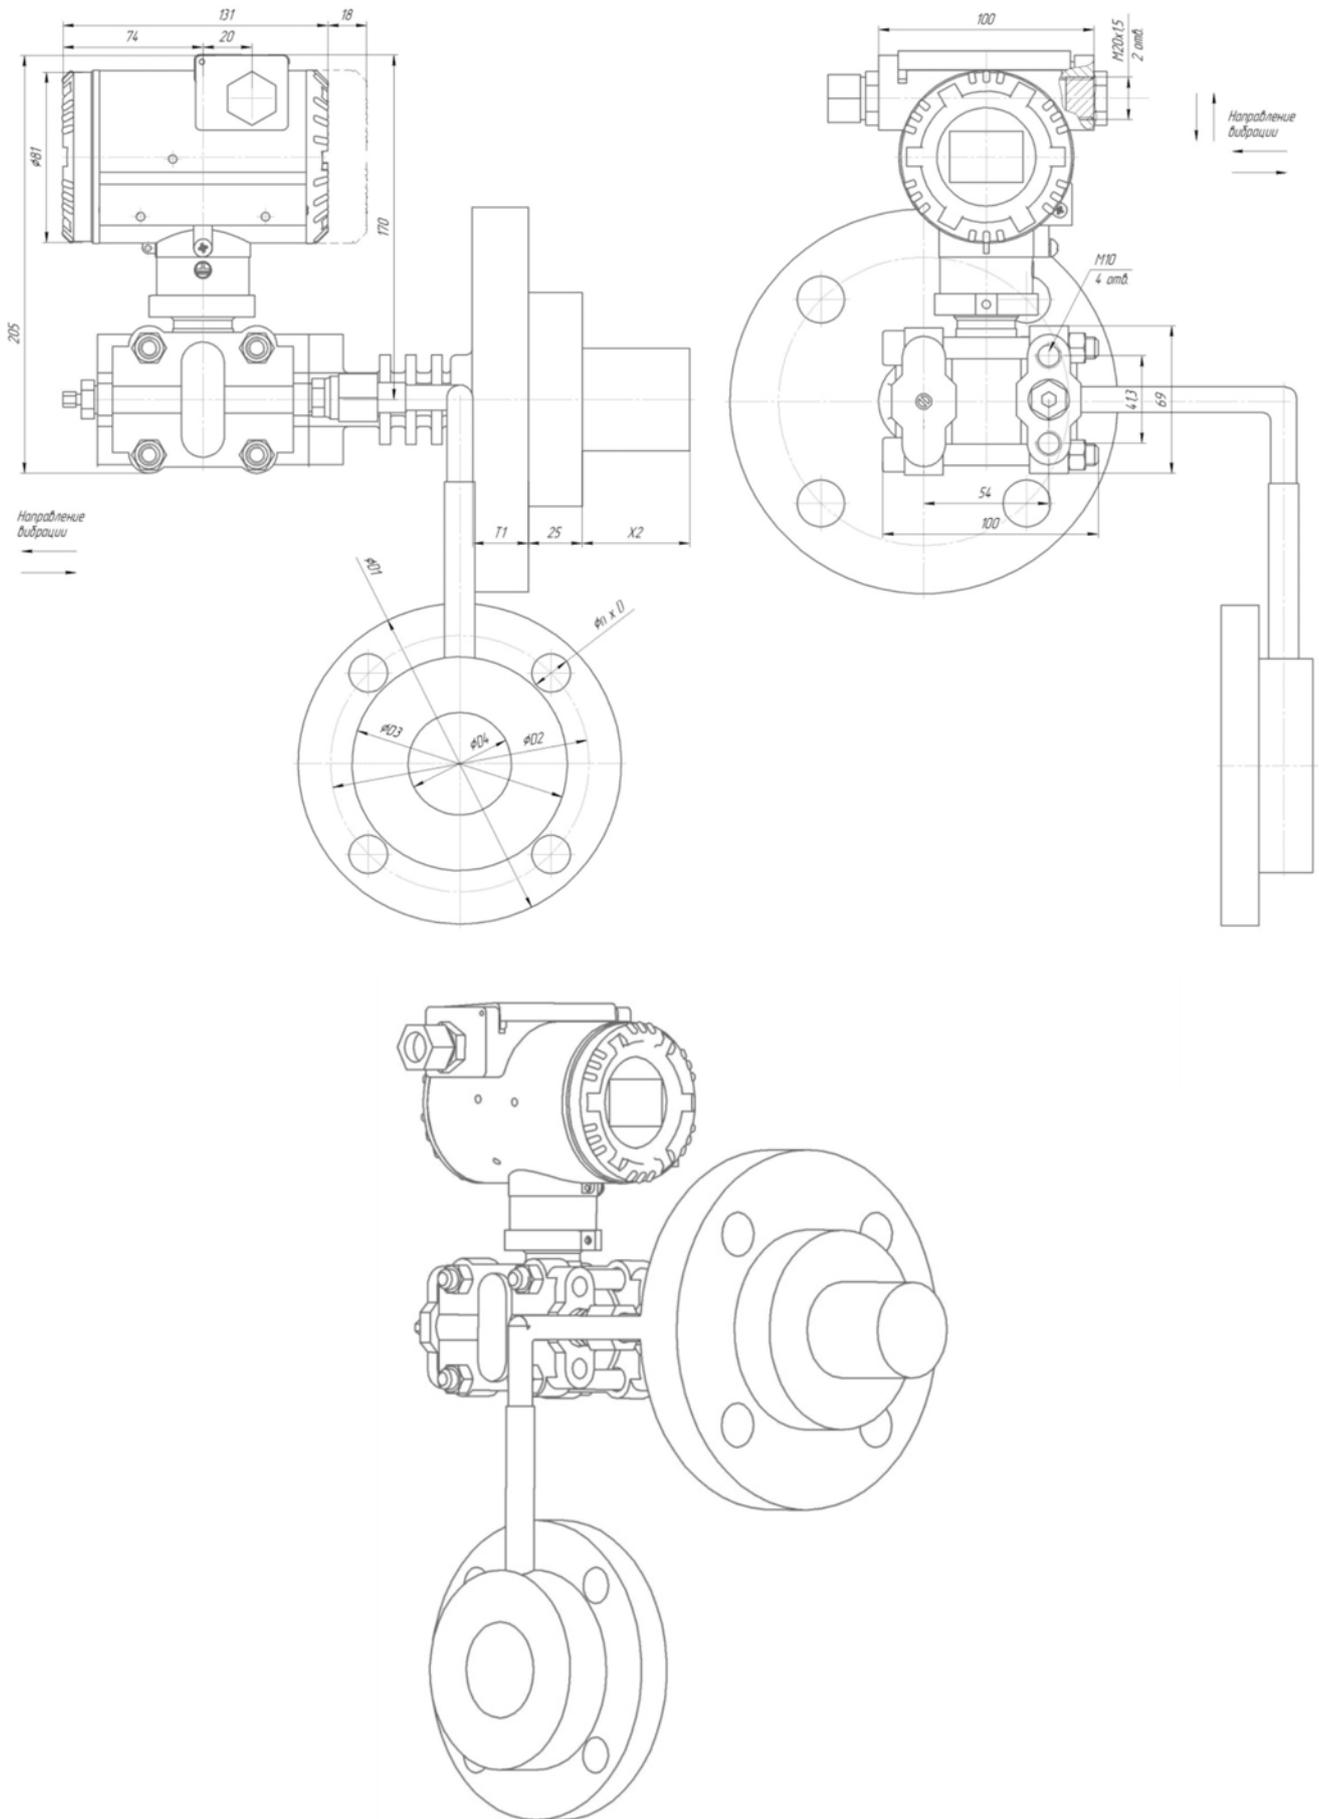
Габаритные, присоединительные размеры ЭМИС-БАР 185, 188 с нулевой длиной капилляра плюсовой камеры
